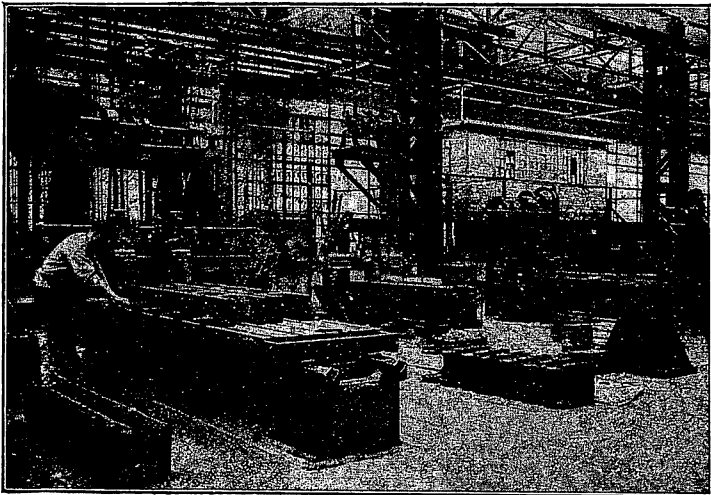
Bedienung mehrerer Hobelmaschinen durch einen Arbeiter.
